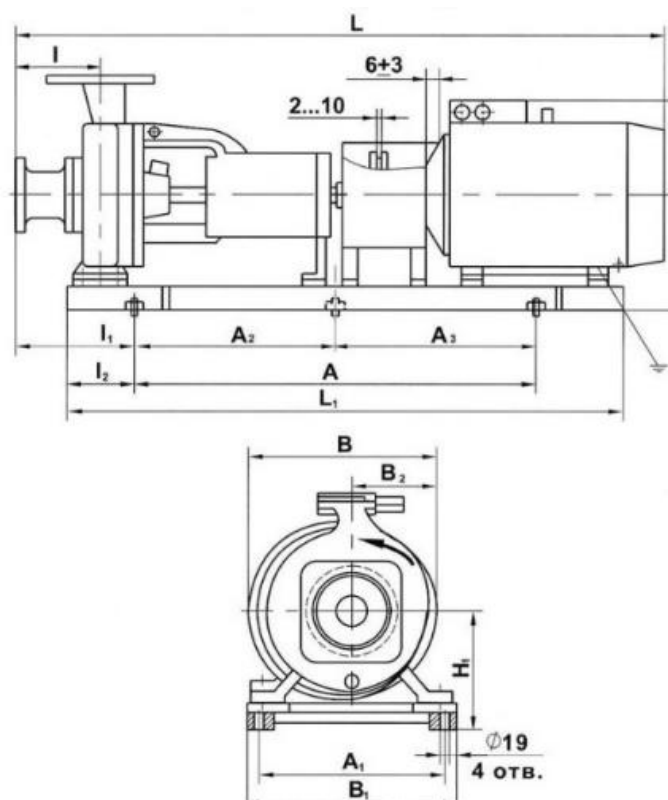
Габаритные и присоединительные размеры насоса К10080-160
